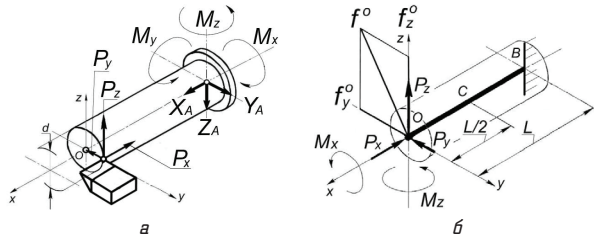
Обробка циліндричного виробу: а — обробка одним різцем на верстаті токарної групи; б — розрахункова схема дії складових сили різання
